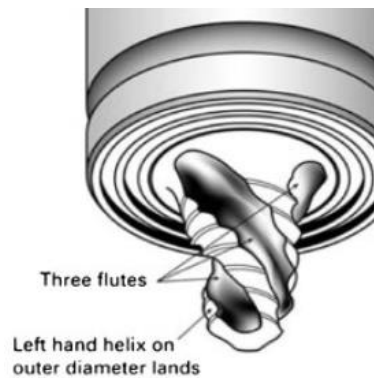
Outil de soudage Flared-Triflute [Rai+2011 ; Zhang+2012].
